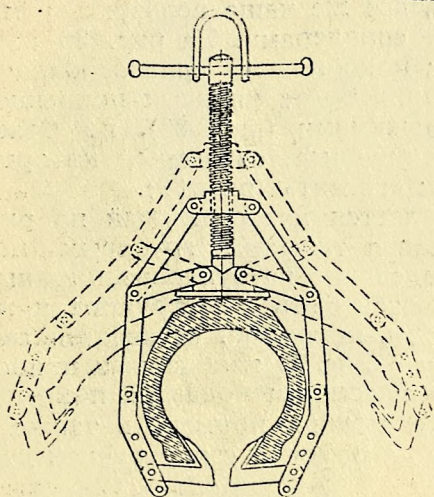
Приспособление для разжимания бортов покрышки при надевании ее на дорн
